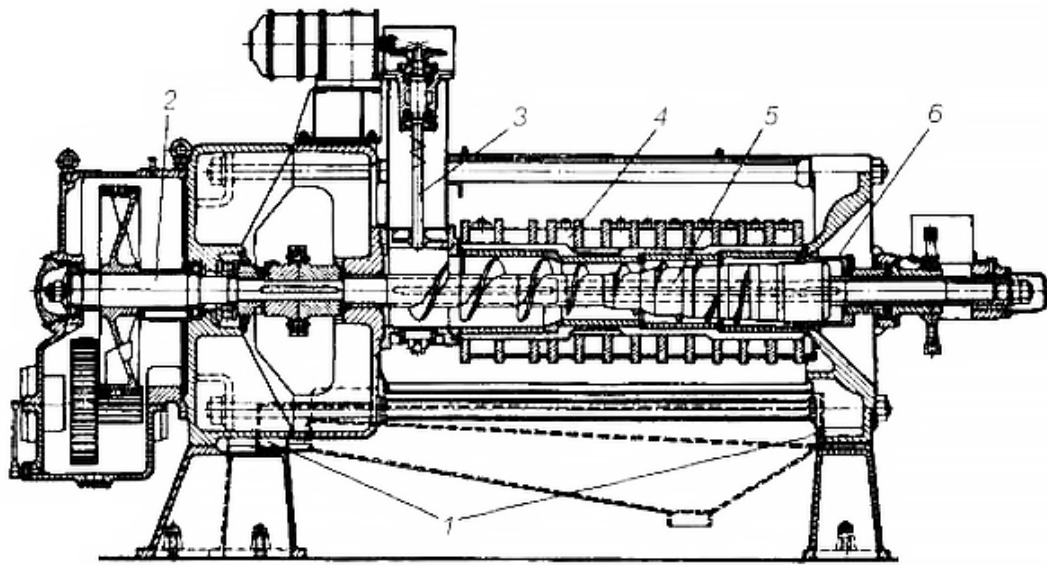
Схема форпреса ФП: 1 – станина; 2 – вал приводний; 3 – регулятор живлення; 4 – зеєрний барабан; 5 – шнековий вал; 6 – регулювальний пристрій.
